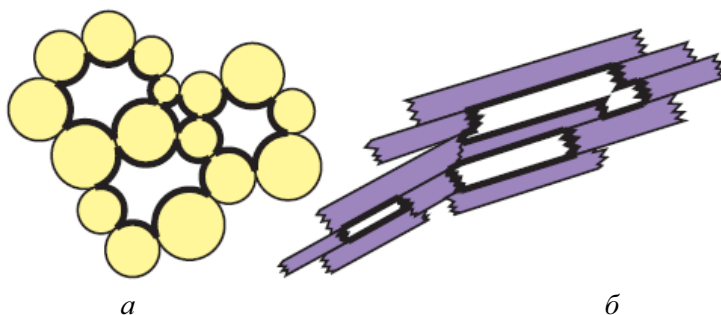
Схематическое изображение пор на поверхностях литейных форм:
